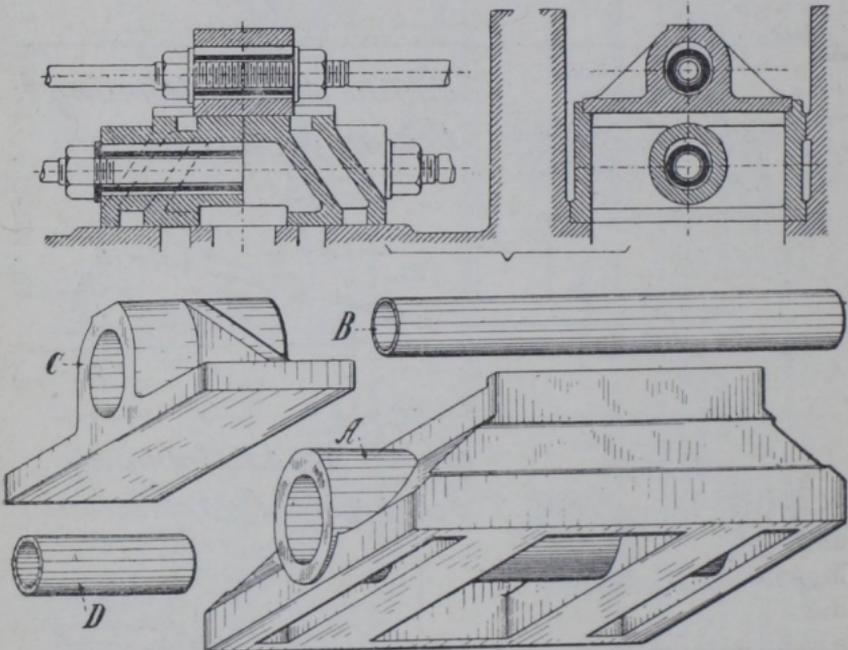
285. Teile zur Doppelschiebersteuerung mit fixer Expansion.
